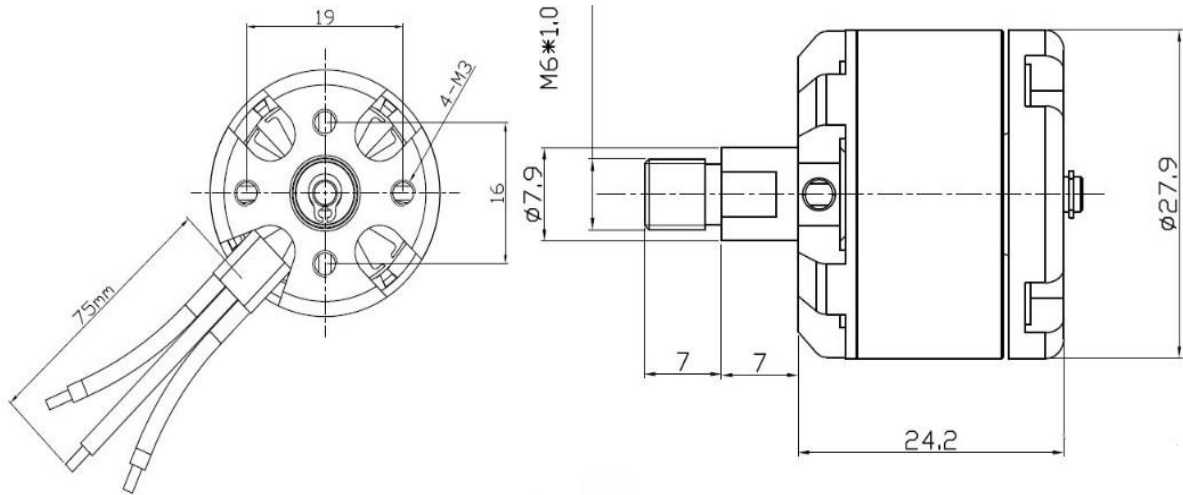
Загальний вид двигуна типу ReadyToSky 2212920KV
